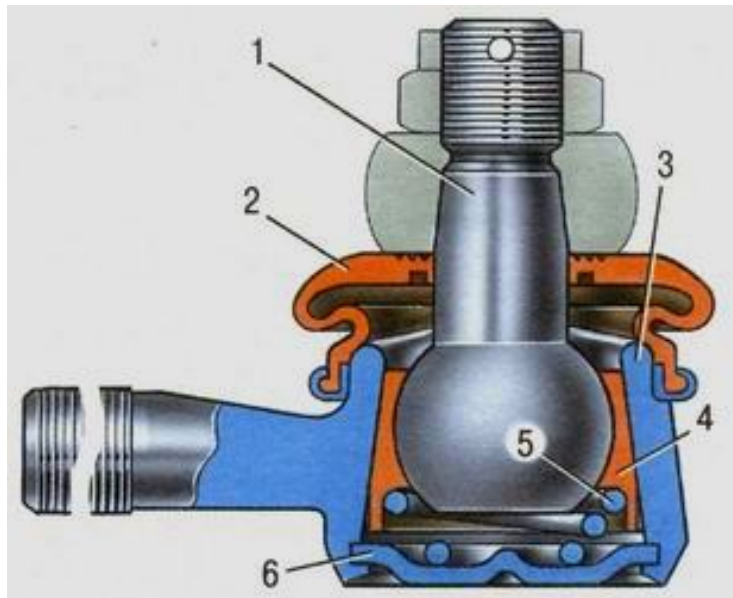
Схема кульового шарніру рульової тяги ВАЗ-2106:
